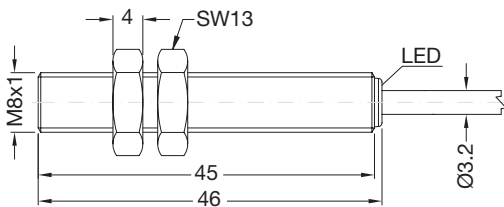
Lange Ausführung, bündiger Einbau, Kabel
